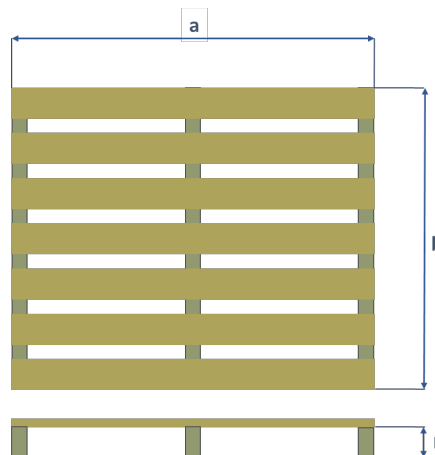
DIMENSIONES PRINCIPALES DEL PALLET
